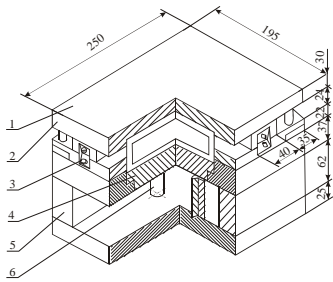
Конструкция блока пресс-форм: 1 – матрица; 2 – верхняя плита; 3 – винты для закрепления формирующей вставки; 4 – подкладная плита; 5 – опоры; 6 – дополнительные опоры
